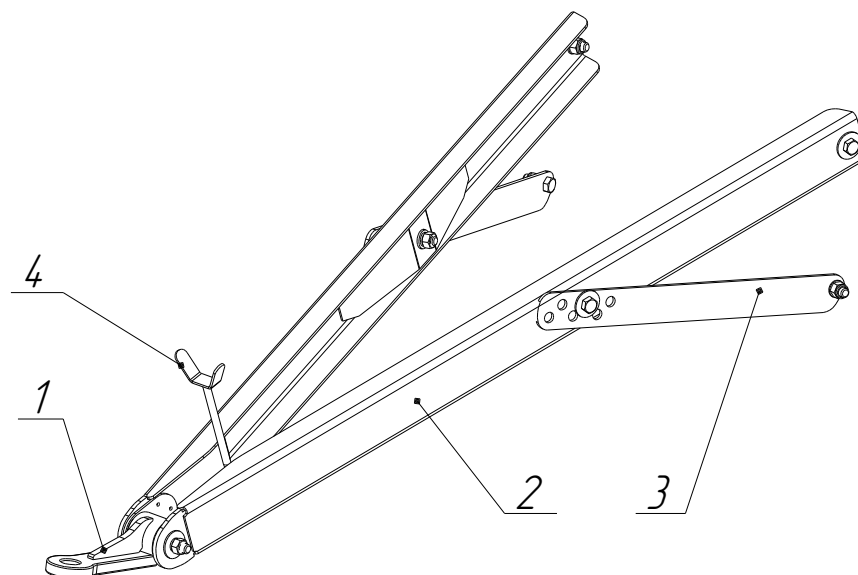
Дышло: 1 – петля дышла; 2 – брус; 3 – раскосина; 4 - опора.
